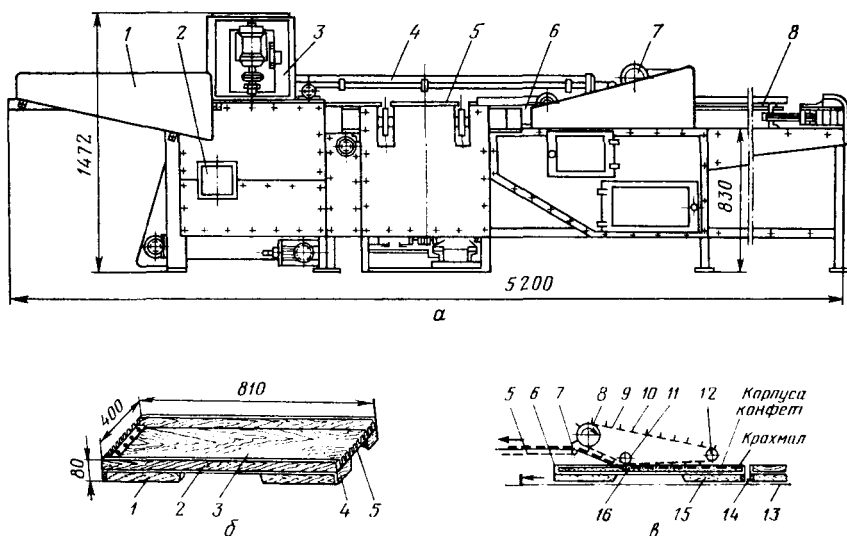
Машина для выборки ликерных корпусов конфет:
